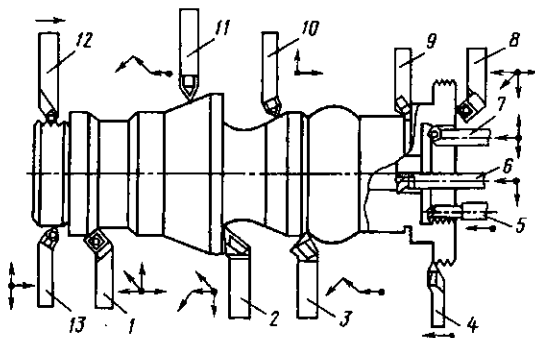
Виды резцов, применяемых на токарных станках с ЧПУ:
